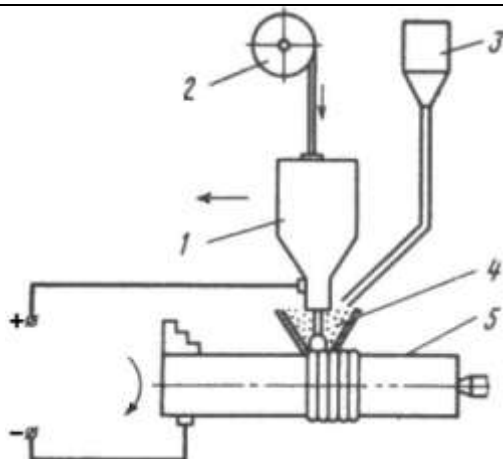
Принципова схема автоматичного електродугового наплавлення під шаром флюсу.
